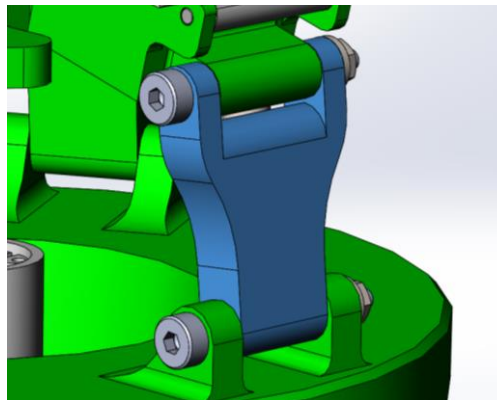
Vista em detalhe do componente braço montado no conjunto.
